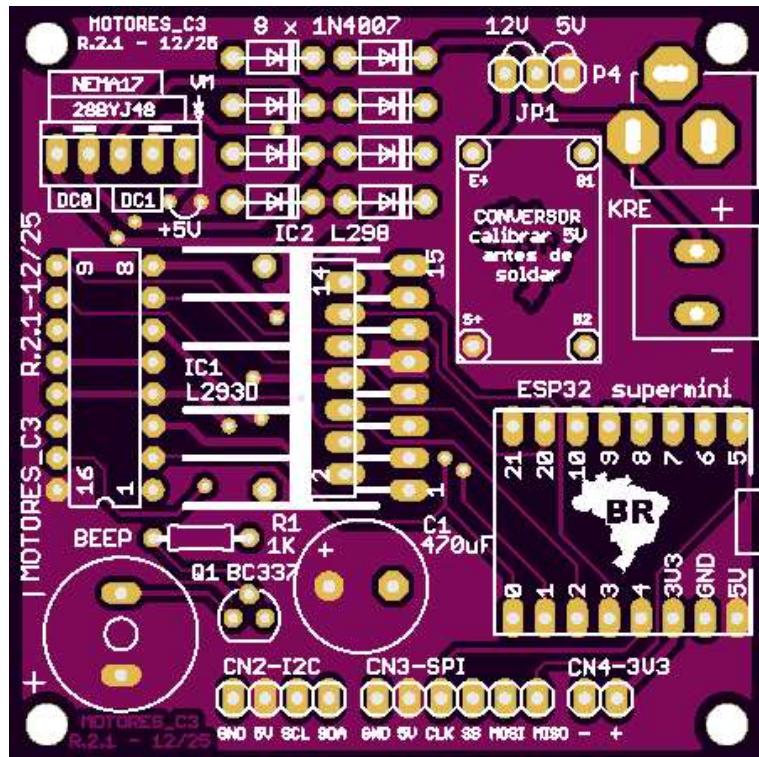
Placa MOTORES\_C3 rev. 2.1 (lado dos componentes)
